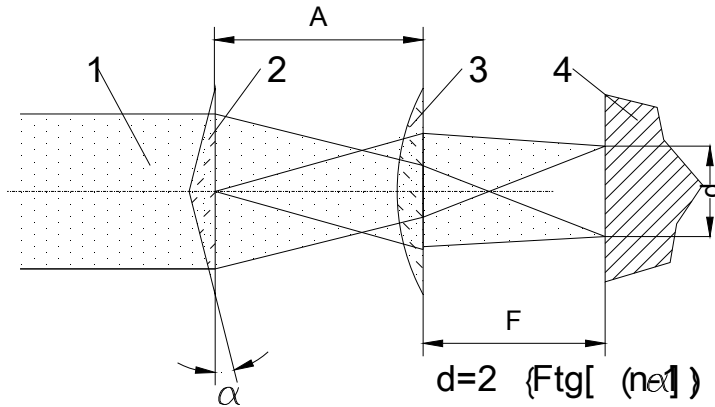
(5.15) . Схема оптичної системи формування пучка кільцевої форми на поверхні заготовки
